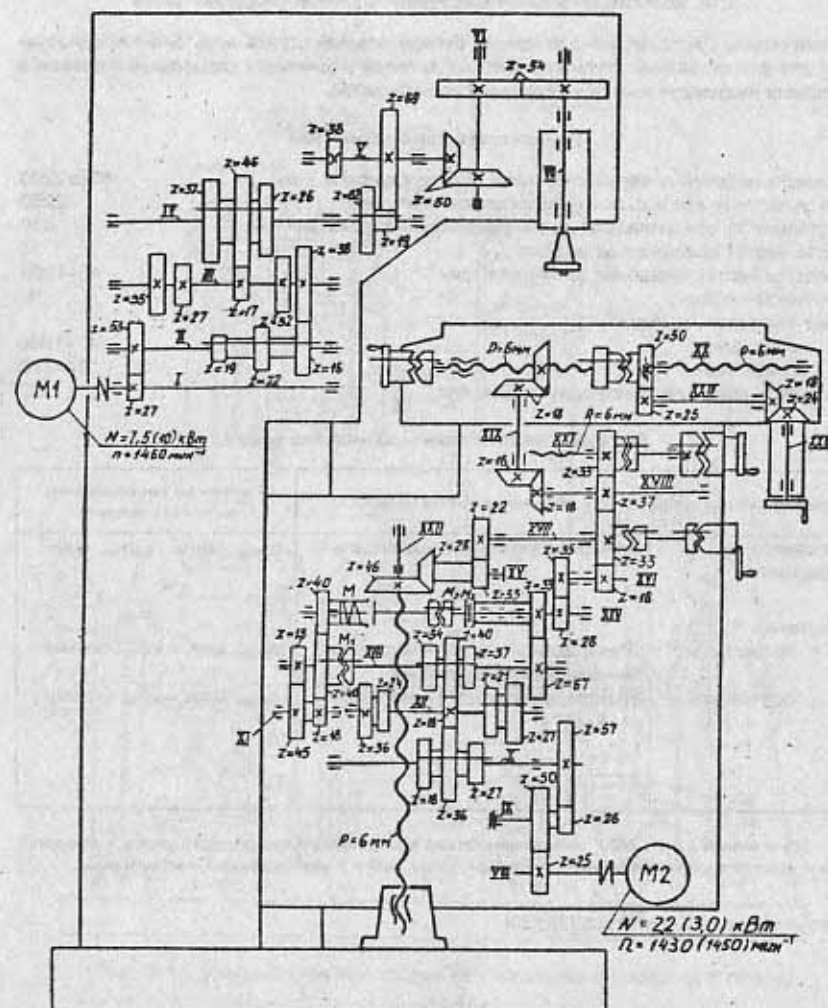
Кинематическая схема вертикально-фрезерного станка мод. 6Р13
